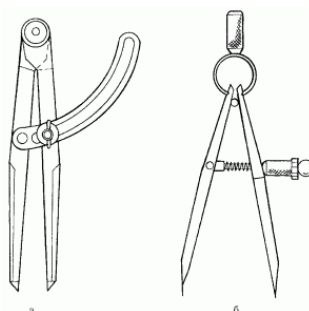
Разметочные инструменты: а – чертилка; б – циркуль.
